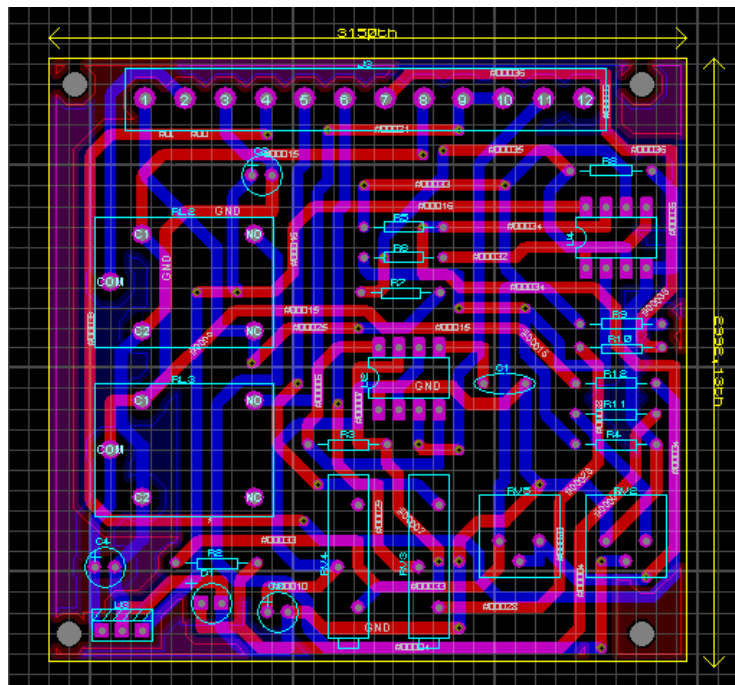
Diseño final de tarjeta de control electrónica PCB (printed circuit board)
